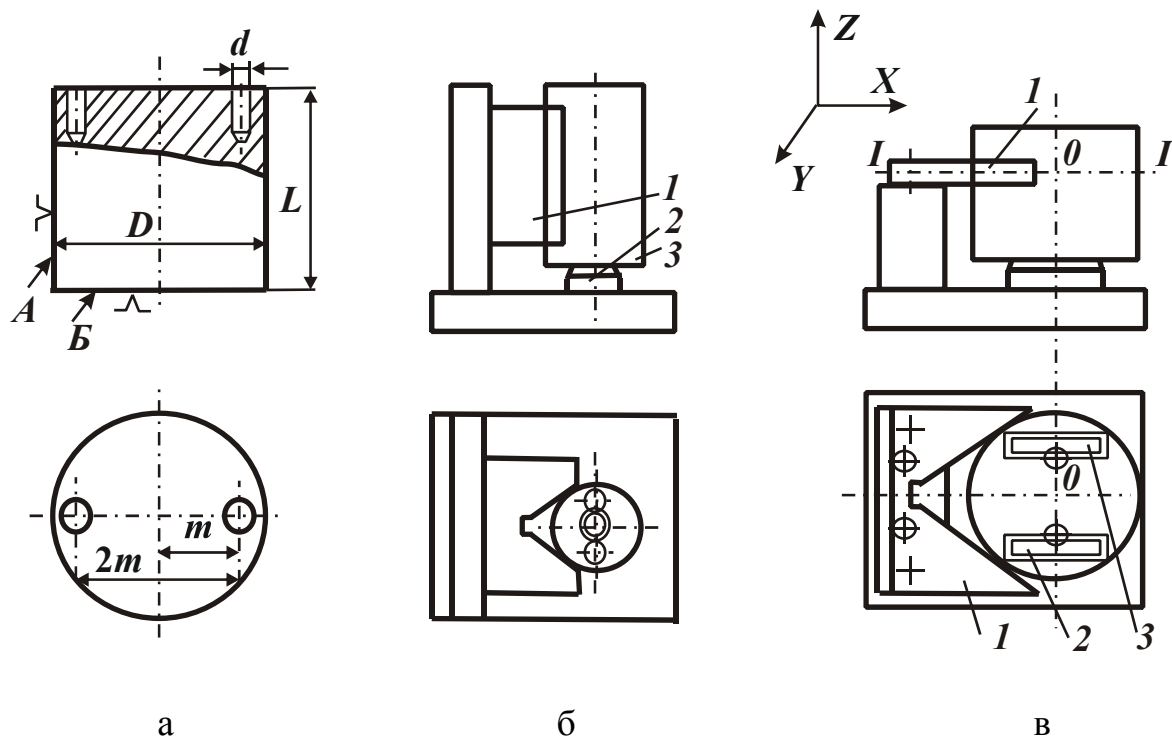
Варианты базирования заготовки плоскостью и наружной цилиндрической поверхностью, ось которой перпендикулярна плоскости.
